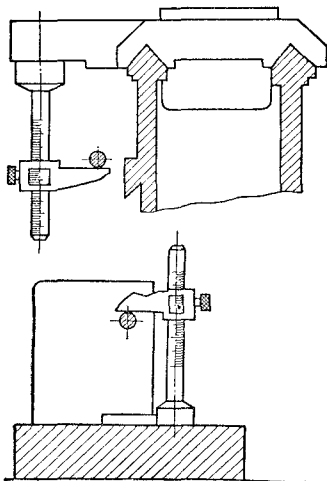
Разметка центра гайки салазок токарного станка специальным керном.
